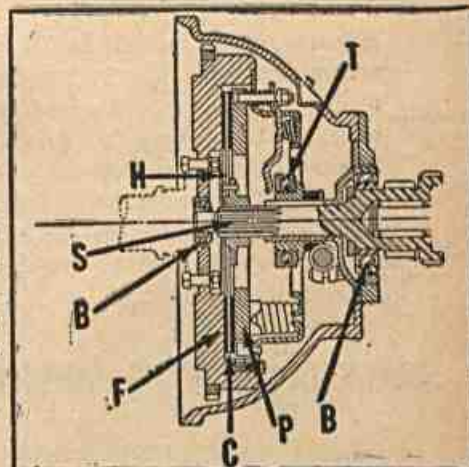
As peças da embreagem que devem ser cuidadosamente examinadas: H — disco da embreagem. S — eixo de transmissão. B — coxim. F — volante. C — guarnições do disco. P — placa de pressão. B — coxim. T — peça de desprendimento.
